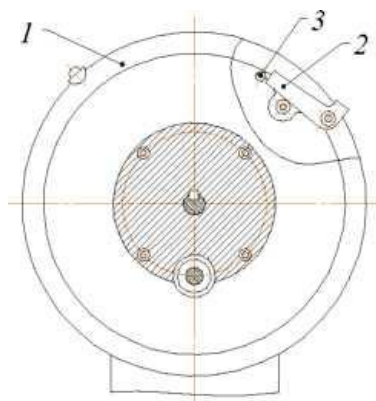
Схема настройки подачи шлифовальной бабки до упору:
